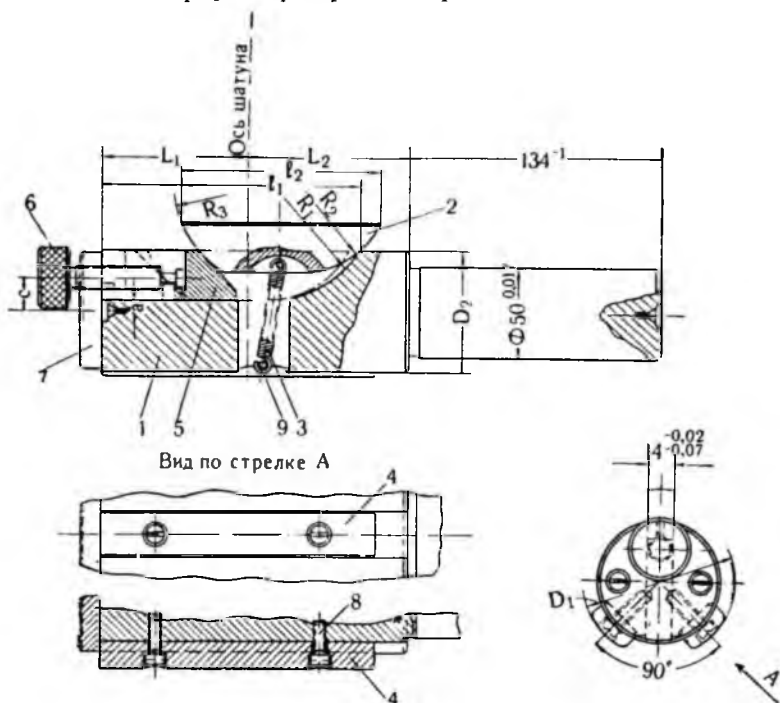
Универсальный палец для установки шатунов на плите прибора для проверки шатунов:
